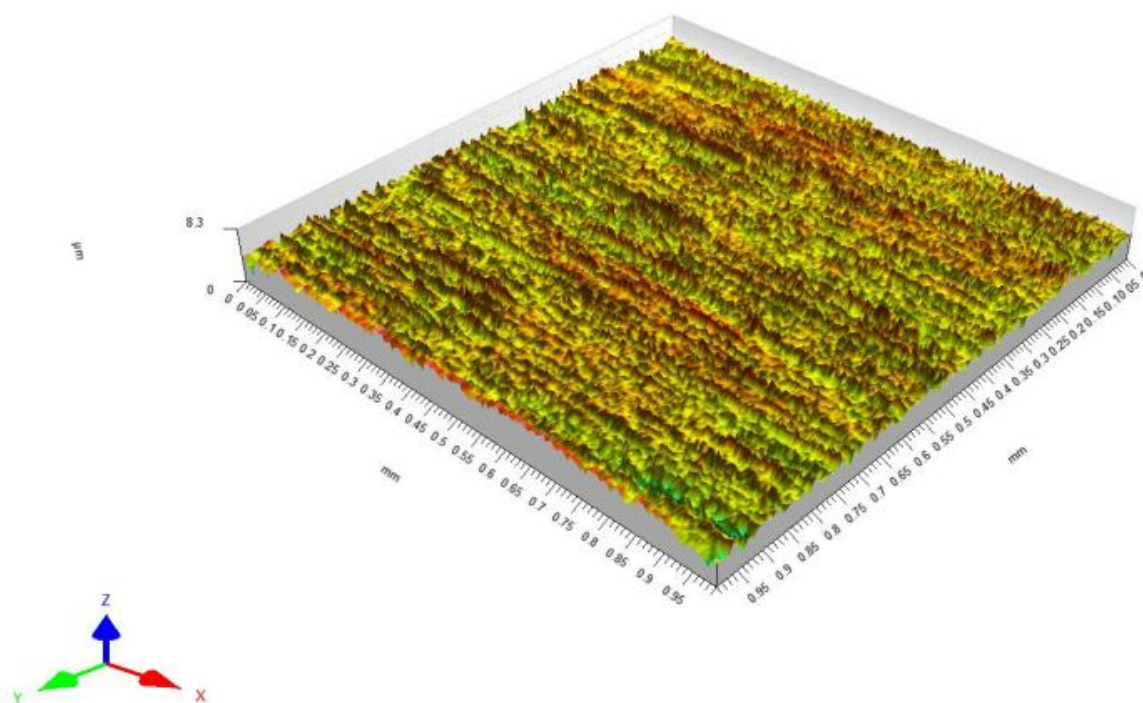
3D zobrazení broušeného povrchu pryže NBR+BR
